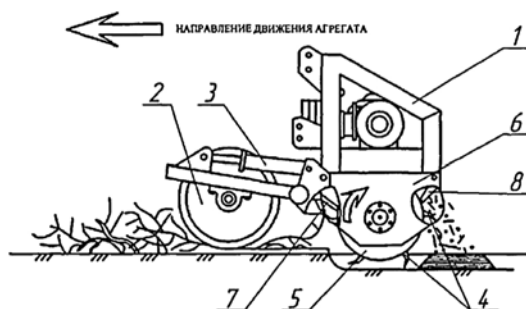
Схема машины для измельчения и заделки щепы в почву [10]: 1 – рама; 2 – трамбовочный барабан; 3 – сервопривод; 4 – ножи; 5 – барабан; 6 – кожух; 7 и 8 – передние и задние контрножи
